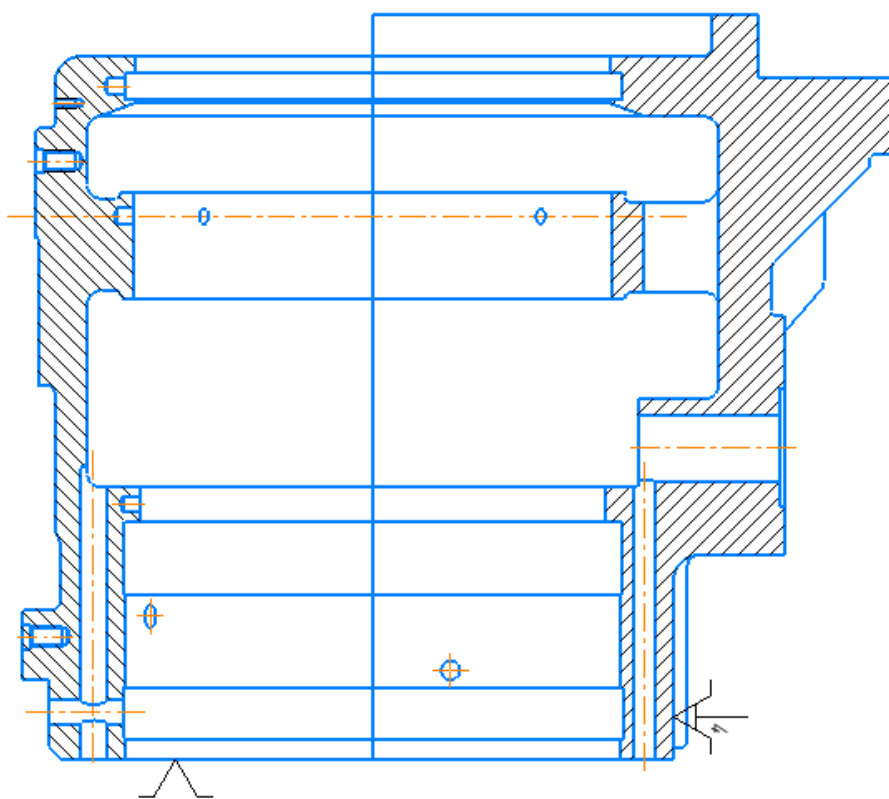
Базирование заготовок «корпус радиально-упорного подшипника» и «крышки радиально-упорного подшипника» в 4-х кулачковом патроне
